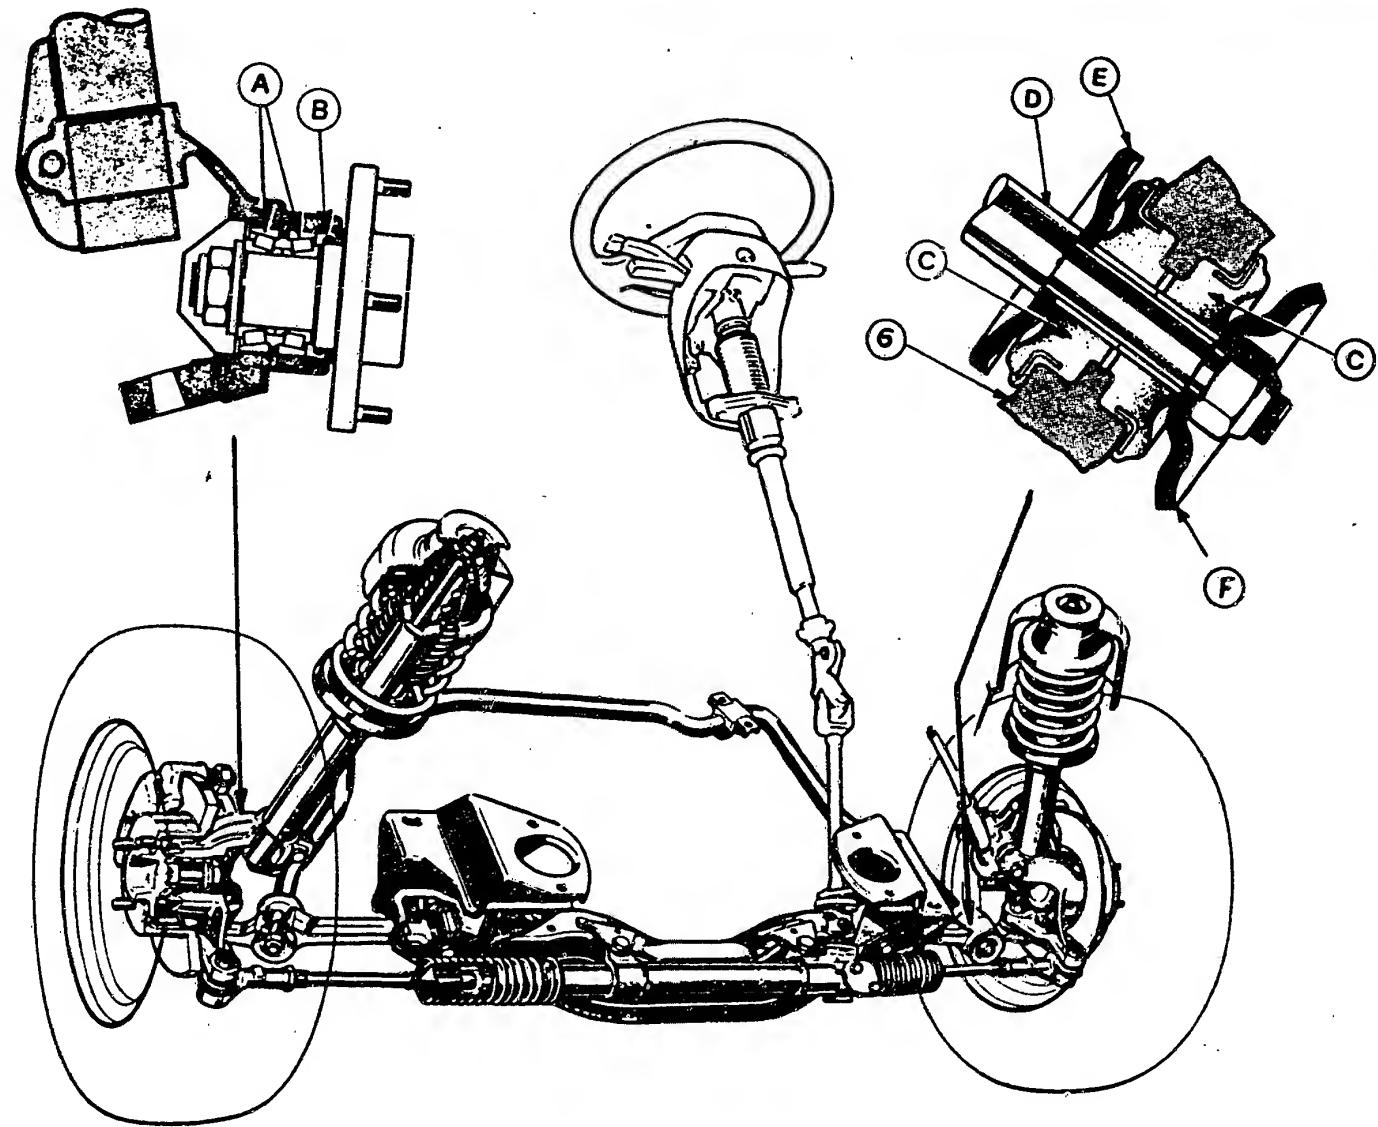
Die Vorderachse mit Aufhängungs- und Lenkungselementen. Es bedeuten: A Schrägrollenlager – B Dichtring – C geteilte Gummibüchse – D Stabilisator – E hintere Scheibe – F vordere Scheibe – G Querlenker.
